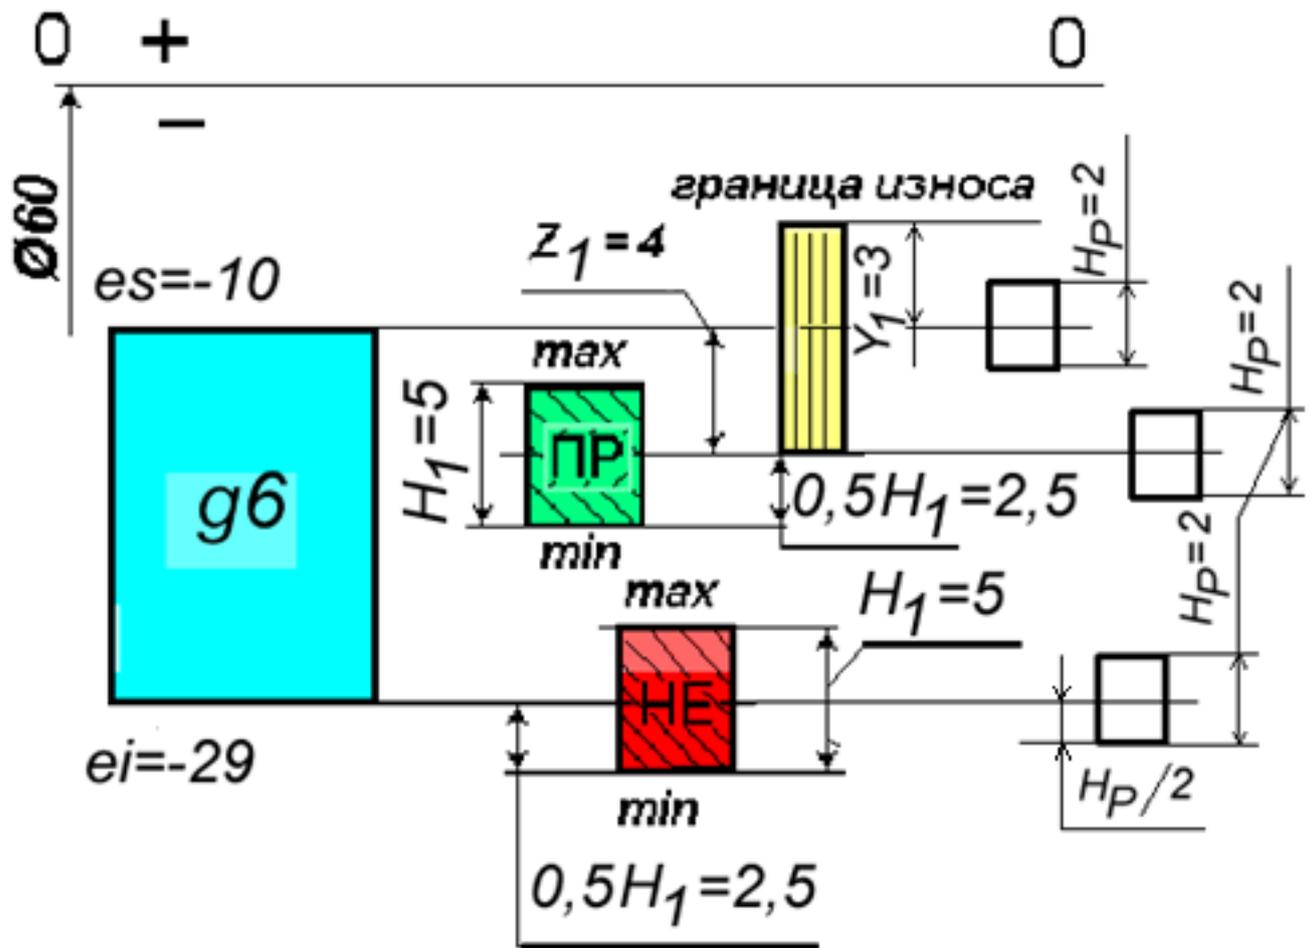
Поля допусков калибр-скобы, для поля допуска g6.
